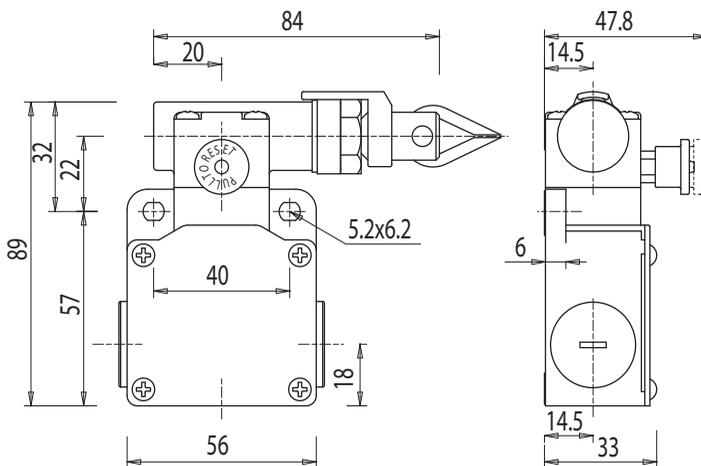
Dimensiones ERS200-MxC3x-HAR en mm
